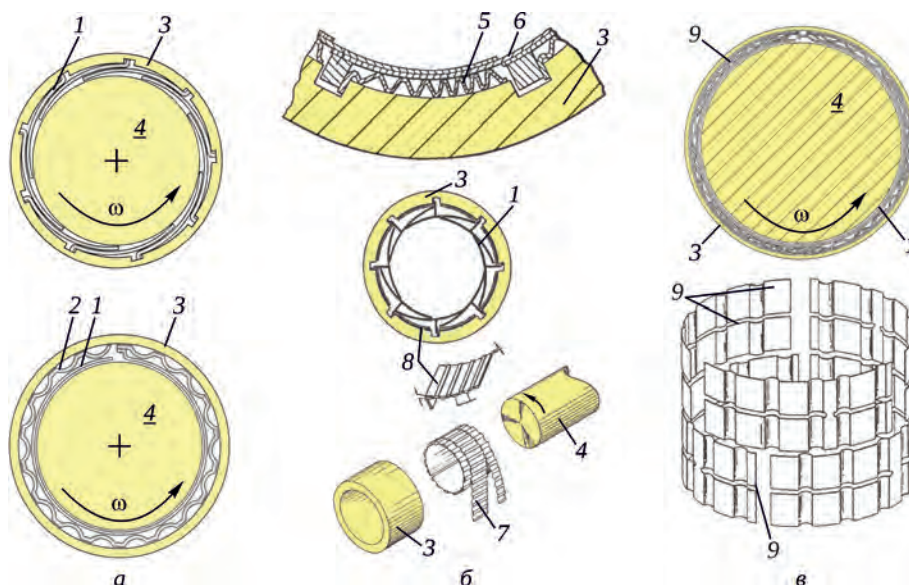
Конструктивные особенности газодинамических подшипников разного поколения [5]: а – первого; б – второго; в – третьего; 1 – лепесток; 2 – гофрированный элемент; 3 – обойма; 4 – вал; 5 – гофрированный элемент с переменным шагом гофров; 6 – гладкий лепесток; 7 – составной гофрированный элемент; 8 – упругое основание; 9 – составной гофрированный элемент с переменным шагом гофров
